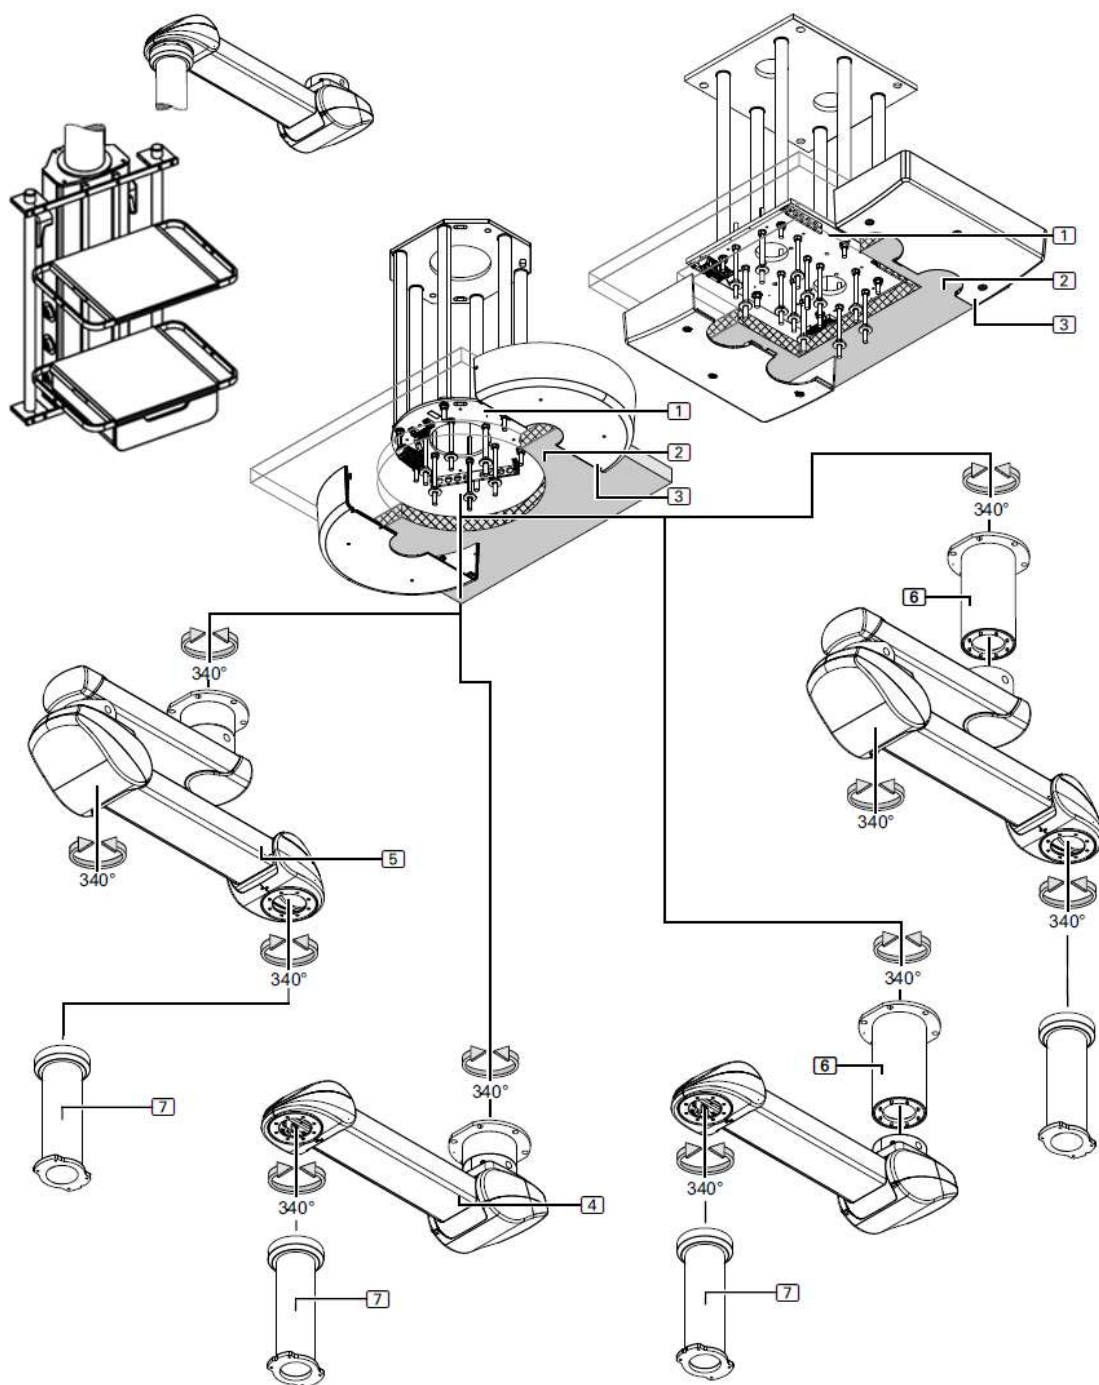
MOTOR SLOUPU AIRPLUS, MOTOR SLOUPU FRICTION
